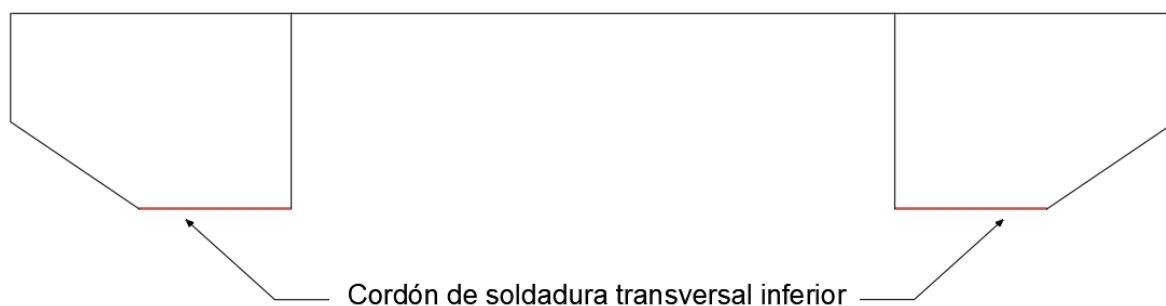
Posición del cordón de soldadura más solicitado frente a fatiga. (elaboración propia)
